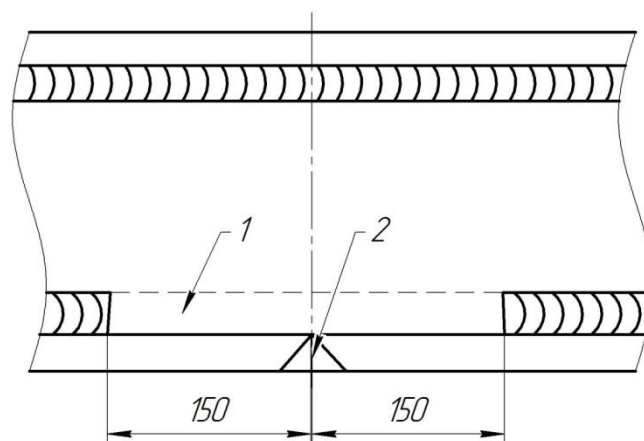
Схема підготовки до заварювання тріщини в полці зварної балки коробчастого перерізу
